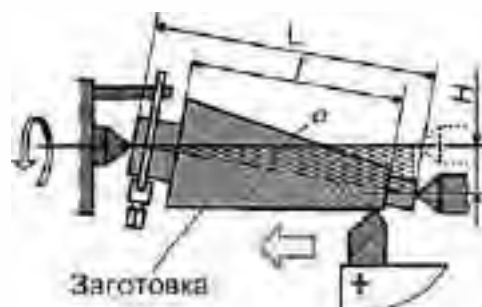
ОБРОБКА ЗОВНІШНЬОЇ КОНІЧНОЇ ПОВЕРХНІ СПОСОБОМ ЗМІЩЕННЯ КОРПУСУ ЗАДНЬОЇ БАБКИ:
